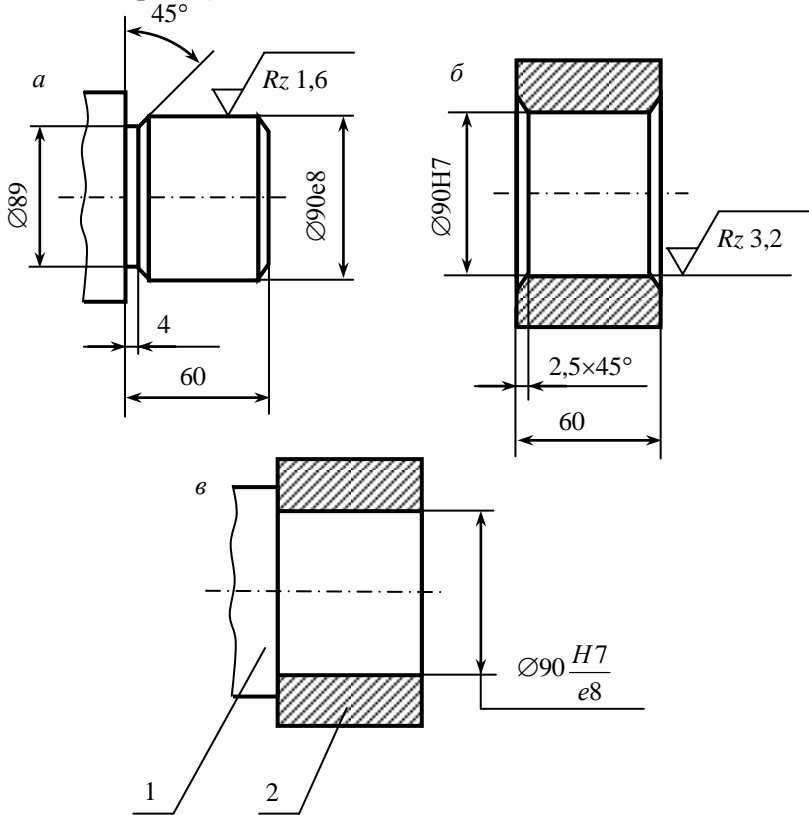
Эскизы: *a* – вала; *б* – втулки; *в* – сборочного чертежа соединения:
